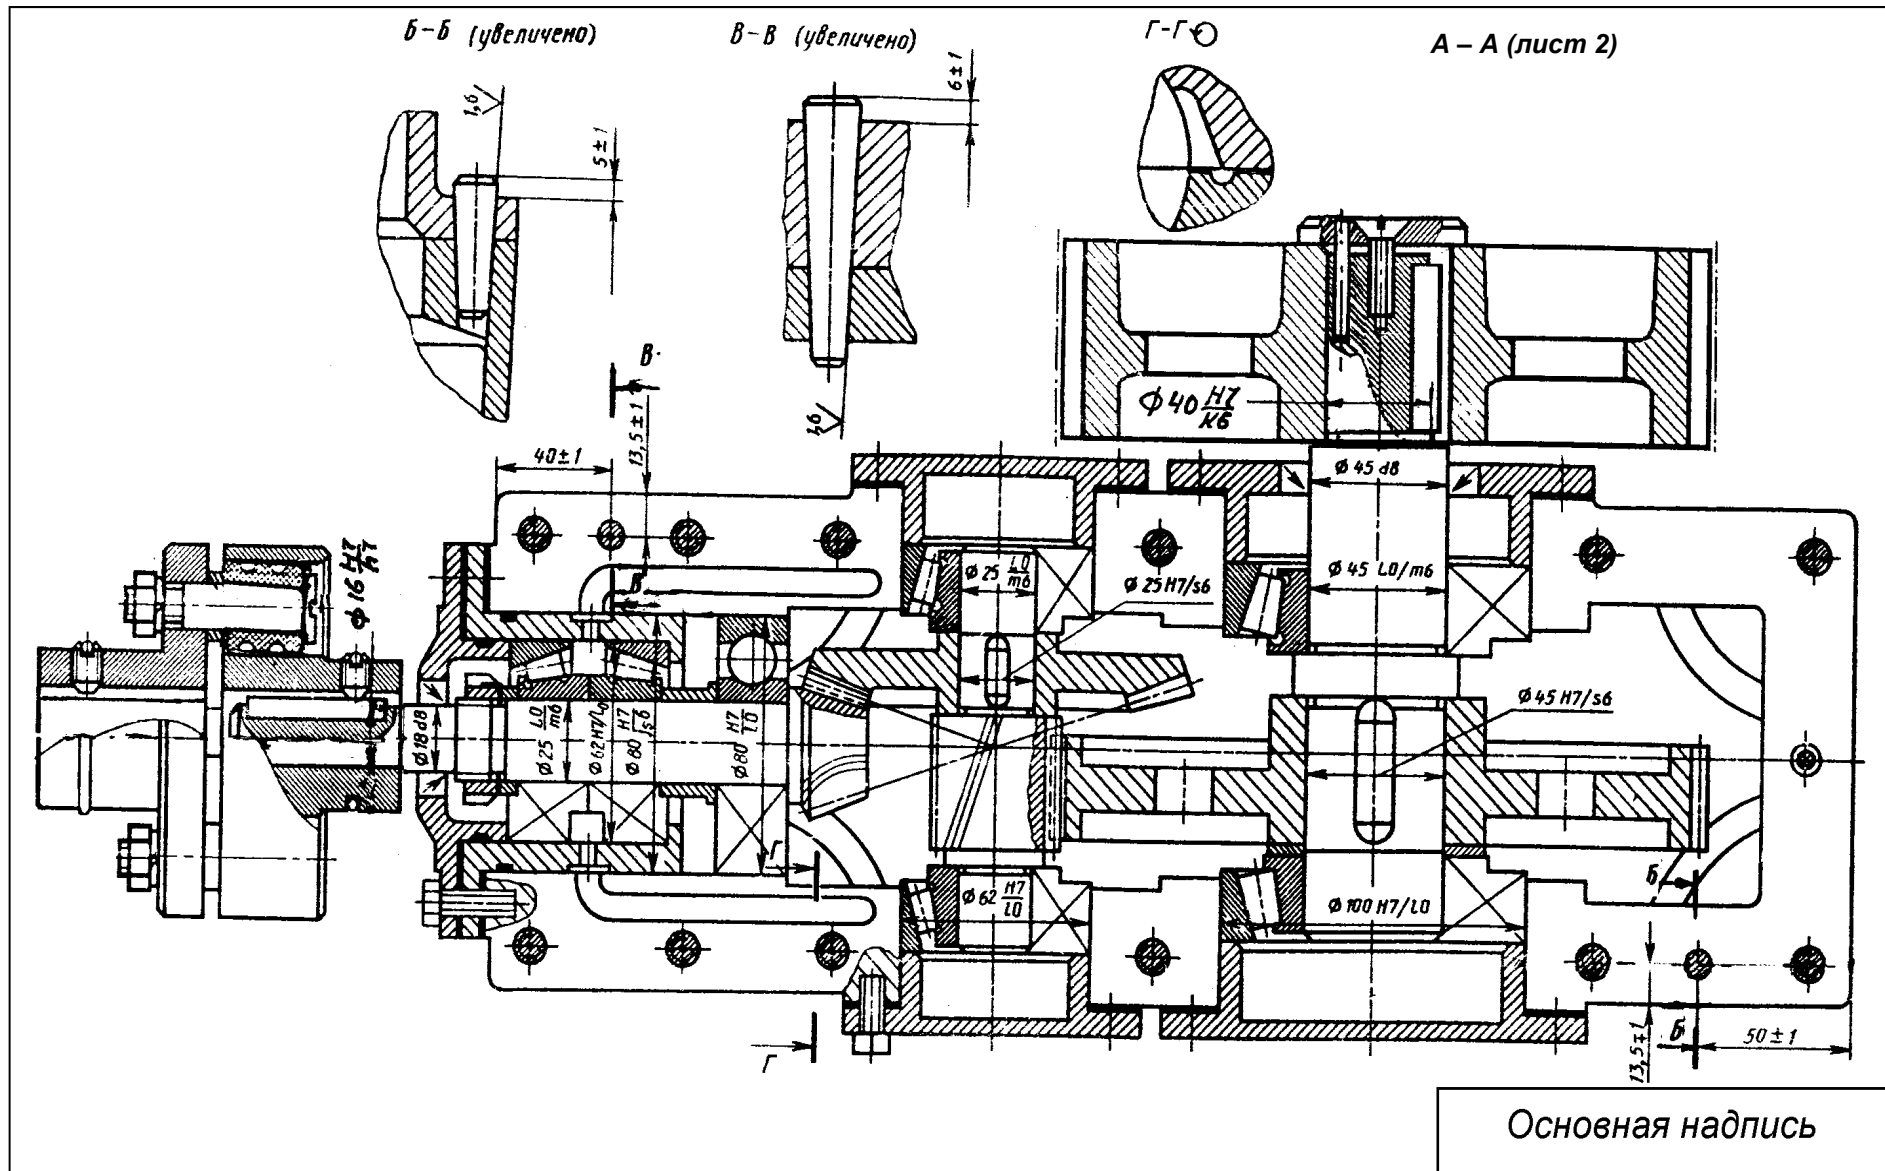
Редуктор коническо-цилиндрический (развертка – лист 1)
